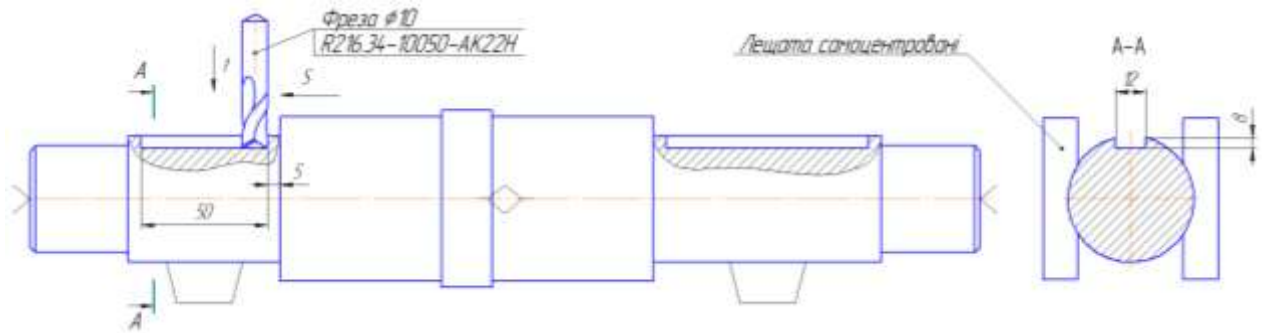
Технологічна схема фрезерування шпонкового паза
